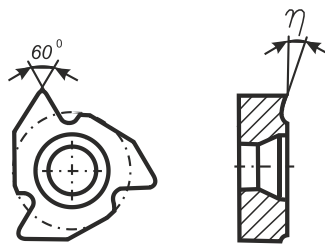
Загальний вигляд нарізевої правої твердосплавної пластини фірми ZCC-СТ для виготовлення нарізи за стандартом API 7
